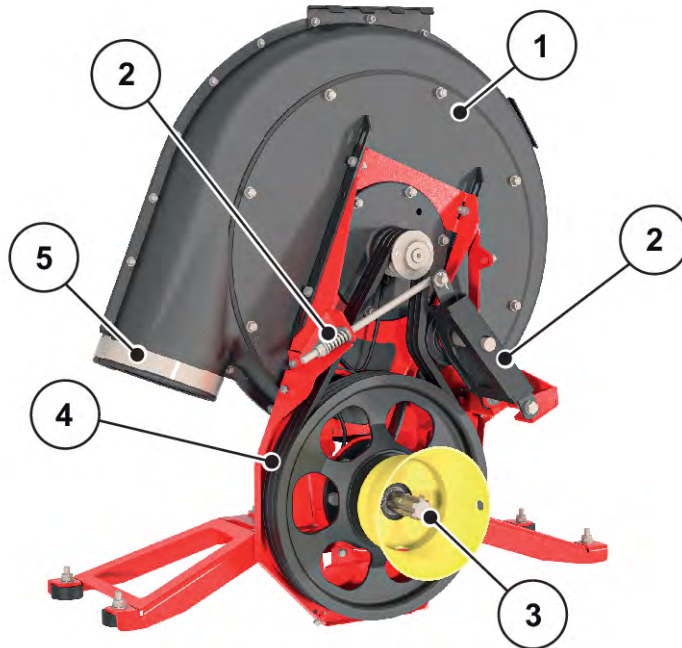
Maskinens komponentgrupper og funksjoner, vifte
